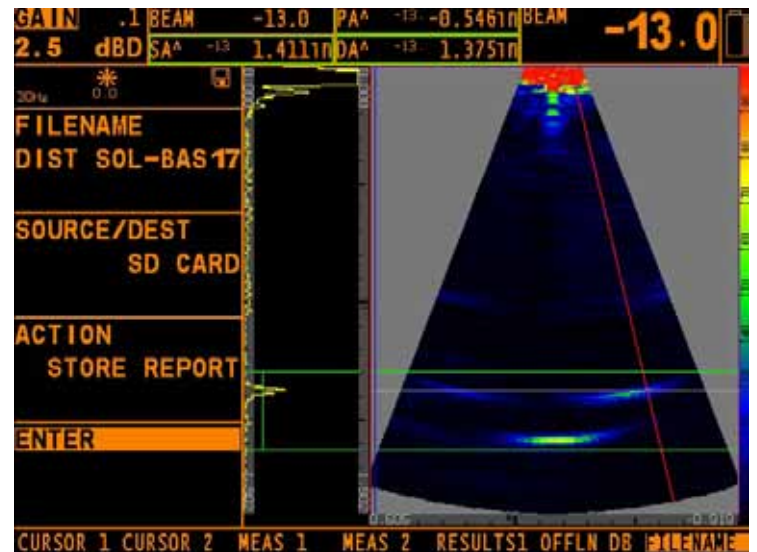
Imagen del Barrido Sectorial con el cursor a -13°, tocando el inicio de la soldadura.
